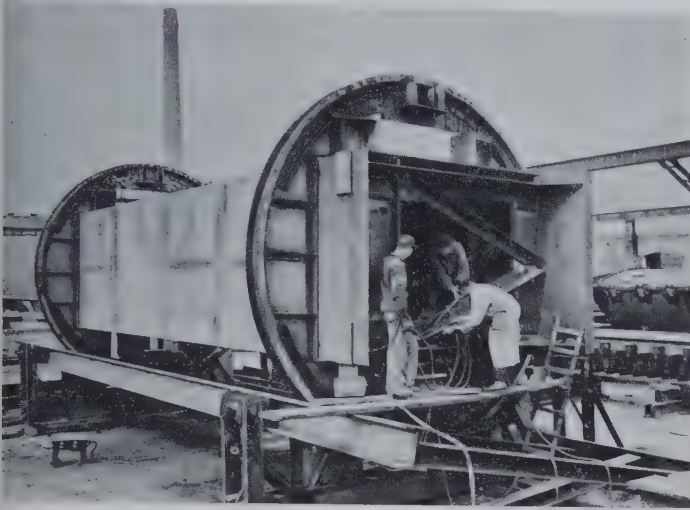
Kastenträger in drehbarer Schweißvorrichtung
